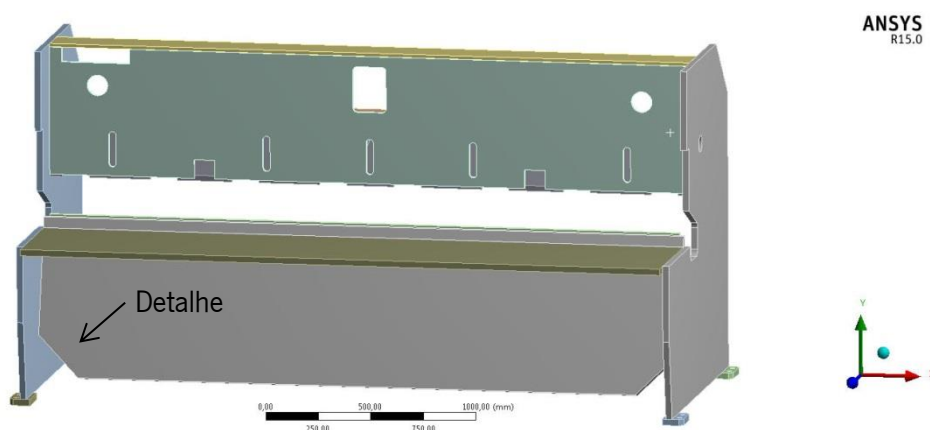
Vista frontal do detalhe da placa do suporte da lâmina na estrutura.
